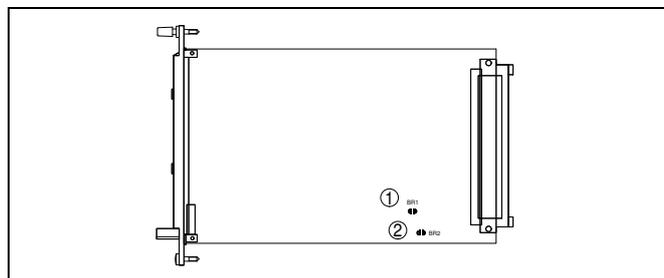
Réglage de la signalisation de défaut - ponts de soudure
